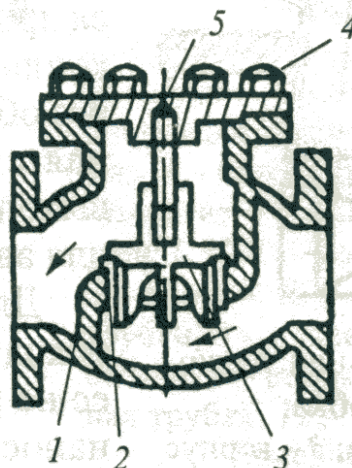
Обратные клапаны: 1 – корпус; 2 – седло; 3 – клапан; 4 – крышка; 5 – направляющий шток клапана
